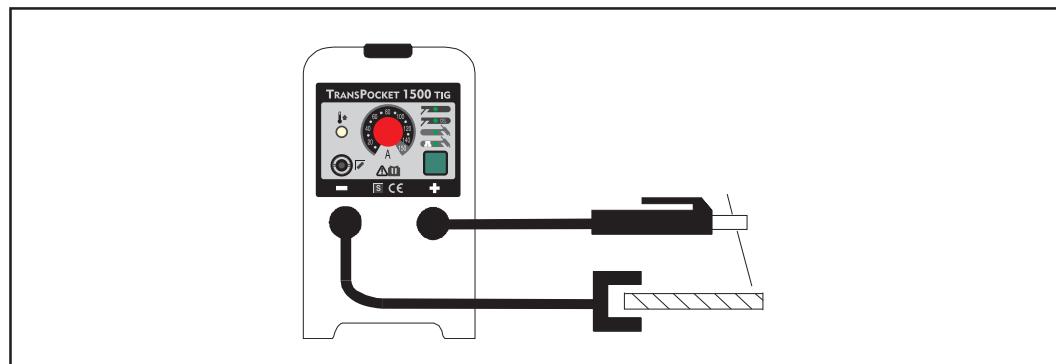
Аппарат TP 1500, приспособленный для сварки стержневым электродом.
